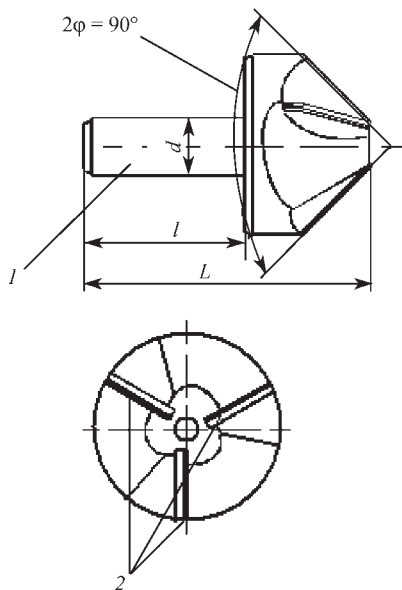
Конструкция конической зенковки, оснащенной пластинами АТП:
